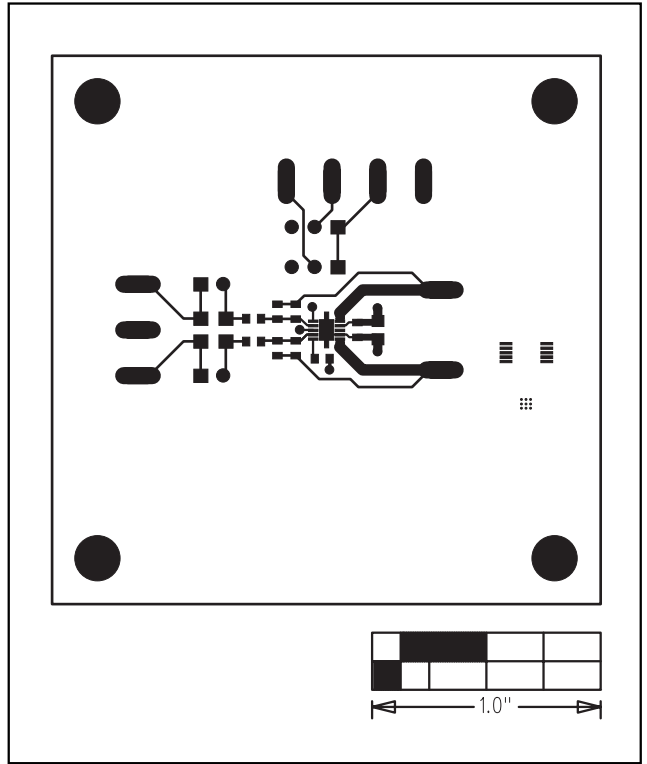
MAX9718A EV 키트 PCB 레이아웃 — 부품 측
